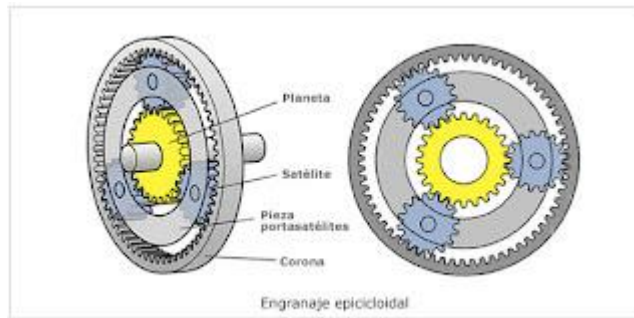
Transmisión de engranajes planetarios. Fuente:[18]
